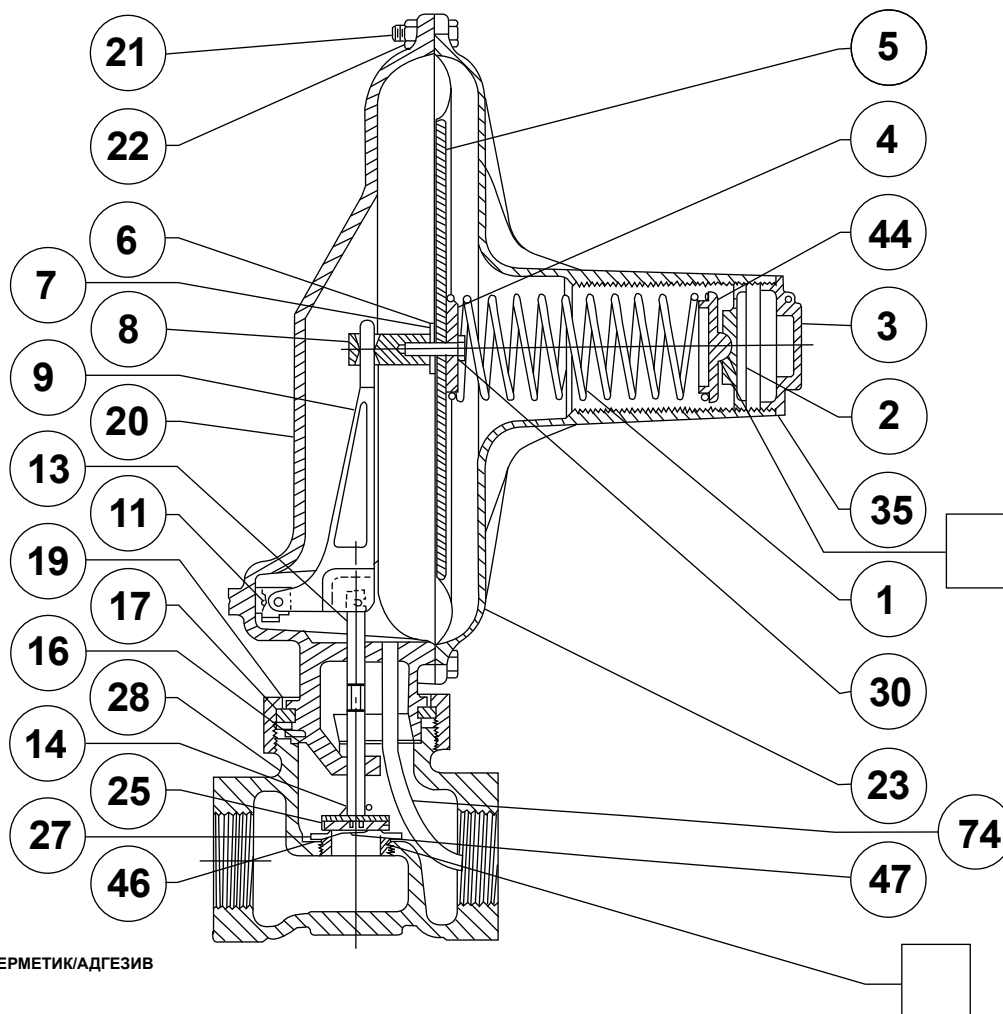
Устройство типа Y692 с легкой регулировочной пружиной в сборе
